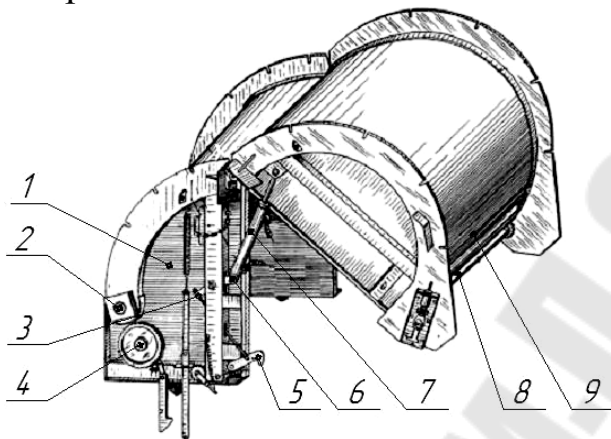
Камера прессования: 1 – камера передняя; 2 – вал ведущий; 3 – тяга; 4 – валец верхний; 5 – защелка; 6 – рычаг; 7 – гидроцилиндр; 8 – ось; 9 – камера задняя
